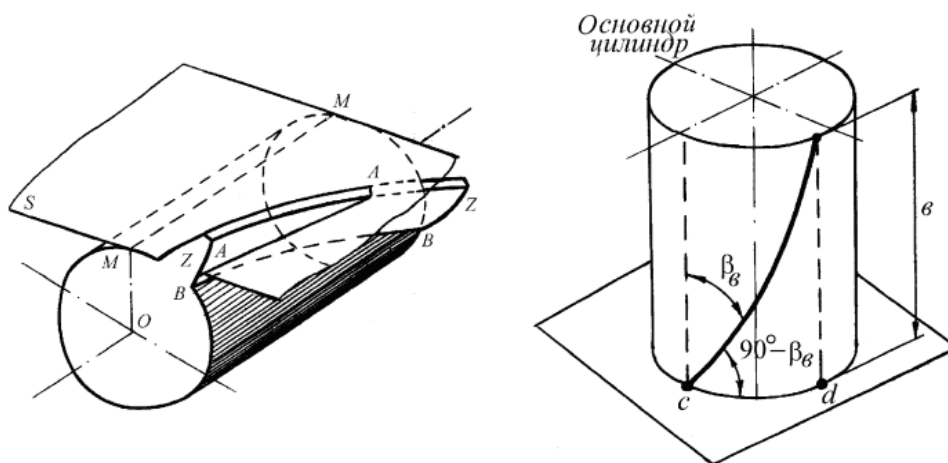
Образование боковой поверхности косоугольного зуба
